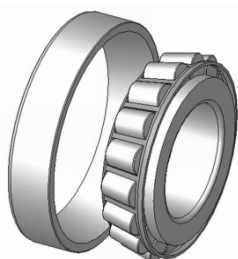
Роликовый конический подшипник (радиально-упорный роликоподшипник)
